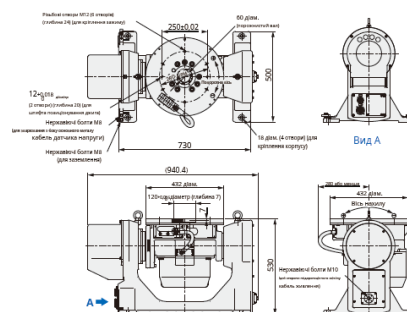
Двоосьовий зварювальний позиціонер MOTOPOS-D250F фірми Yaskawa
